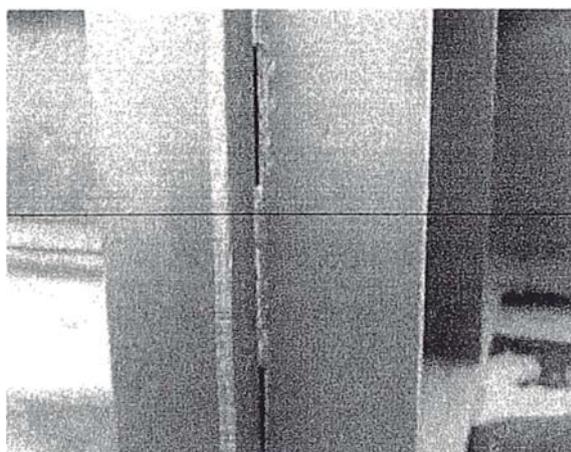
Corrosión en Cavidades – Estructura soldada parcialmente
